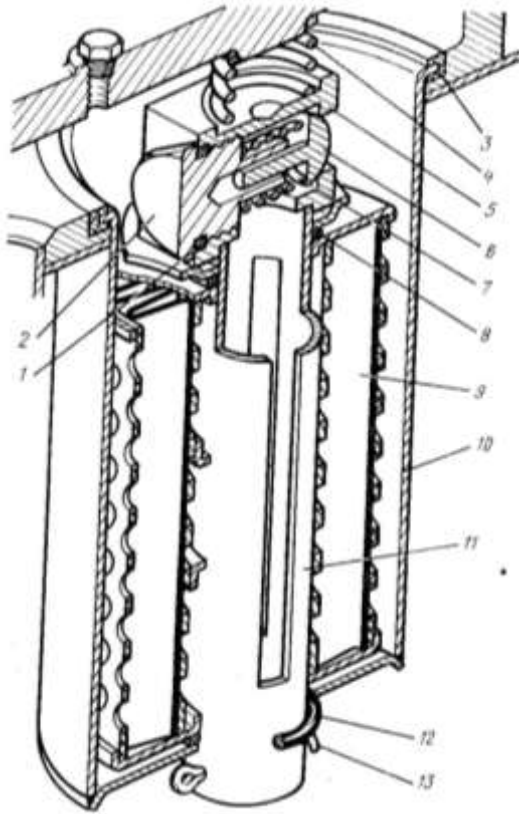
Фильтр малого бака: 1, 8, 12 – кольца; 2 – направляющая клапана; 3 – манжета; 4, 7 – пружины; 5 – корпус; 6 – клапан; 9 – фильтрующий элемент; 10 – корпус фильтра; 11 – труба фильтра; 13 – шплинт
